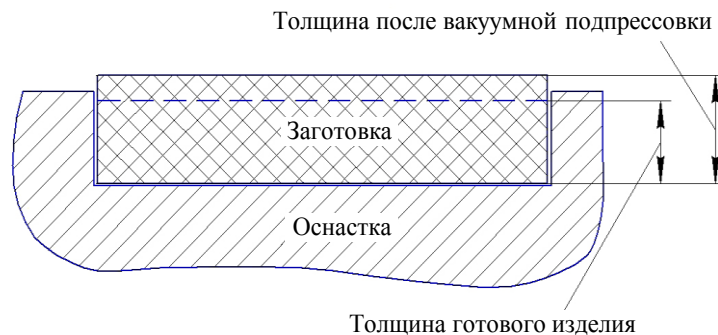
Толстостенная заготовка из полимерного композиционного материала на оснастке
